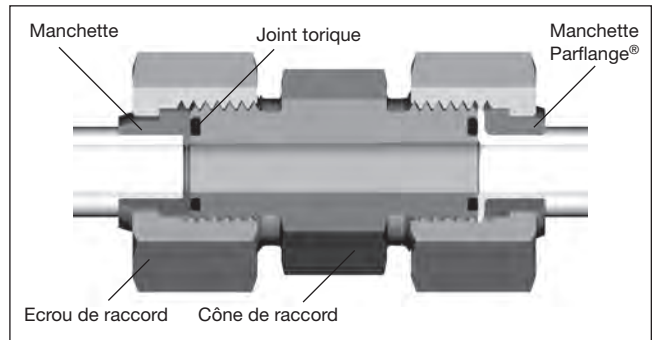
Union tube tube O-Lok® avec manchette brasée (LHS) et manchette Parflange®
